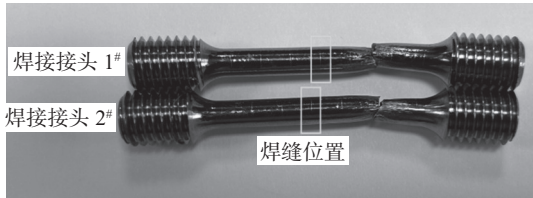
TA18 管摩擦焊接接头拉伸断后试样
